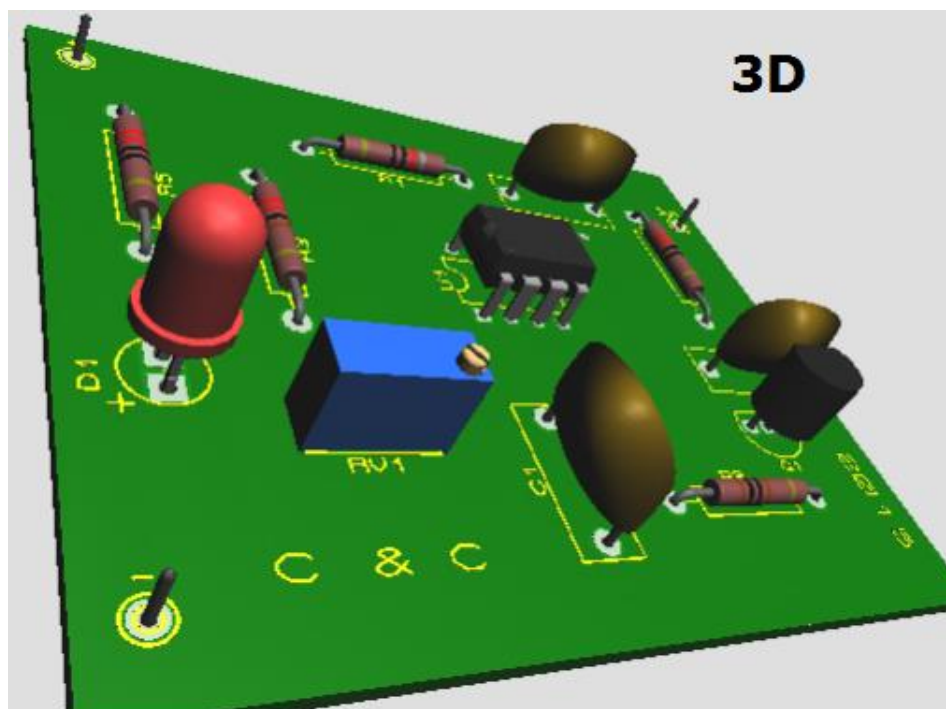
Vista 3D de PCB diseñada para el transmisor.
